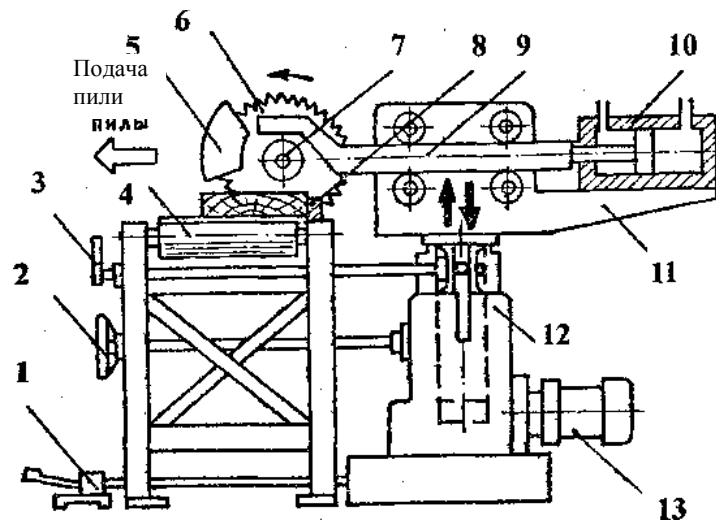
Верстат торцювальний з прямолінійним рухом пили: 1—педаль; 2—маховичок підйому колонки; 3—рукоять затискання колонки; 4—стіл з роликами; 5—огородження; 6—пила; 7—електродвигун; 8—лінійка напрямної; 9—супорт; 10—гідроциліндр; 11—колонка; 12—станина; 13—електродвигун гідроприводу подачі.
